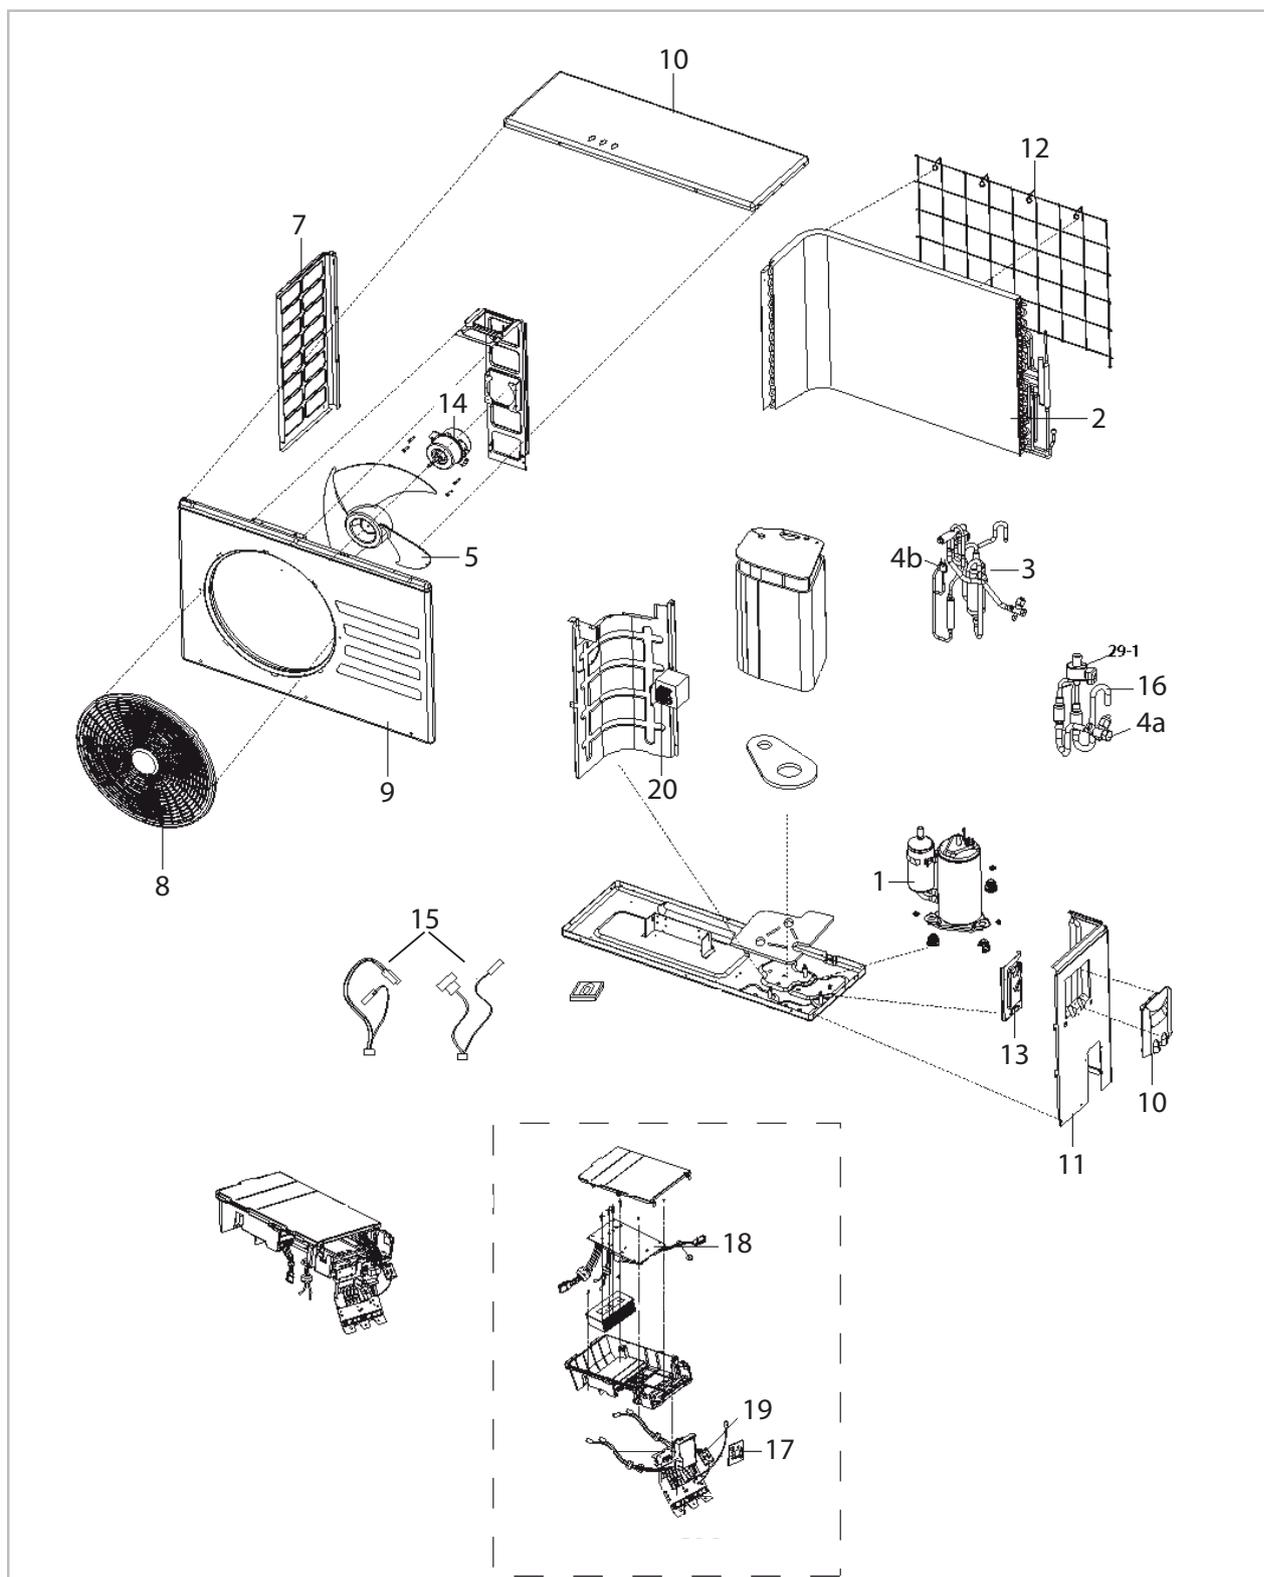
Vue éclatée du module externe WKF/WKF-compact 70
